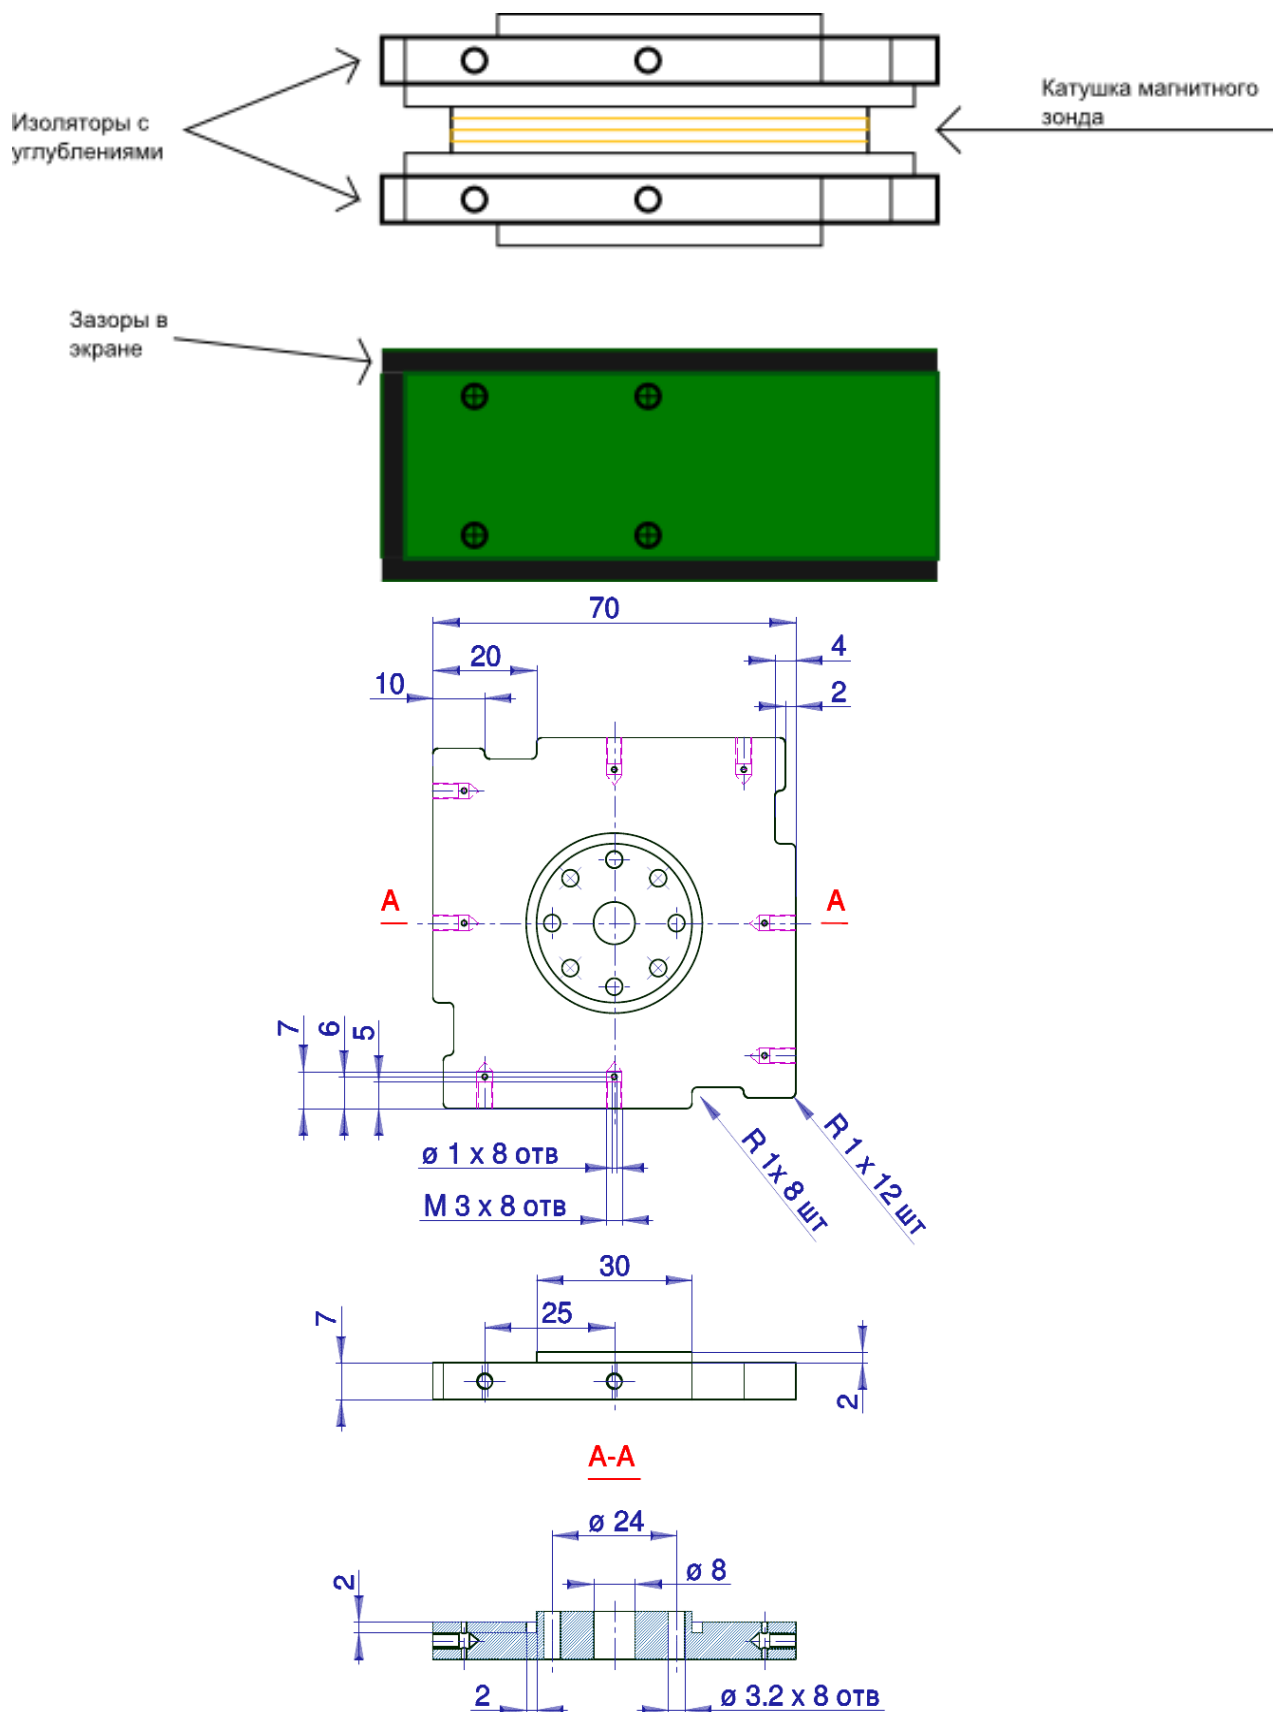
Сверху – схема одиночного магнитного зонда, снизу - чертеж изолятора для него.
